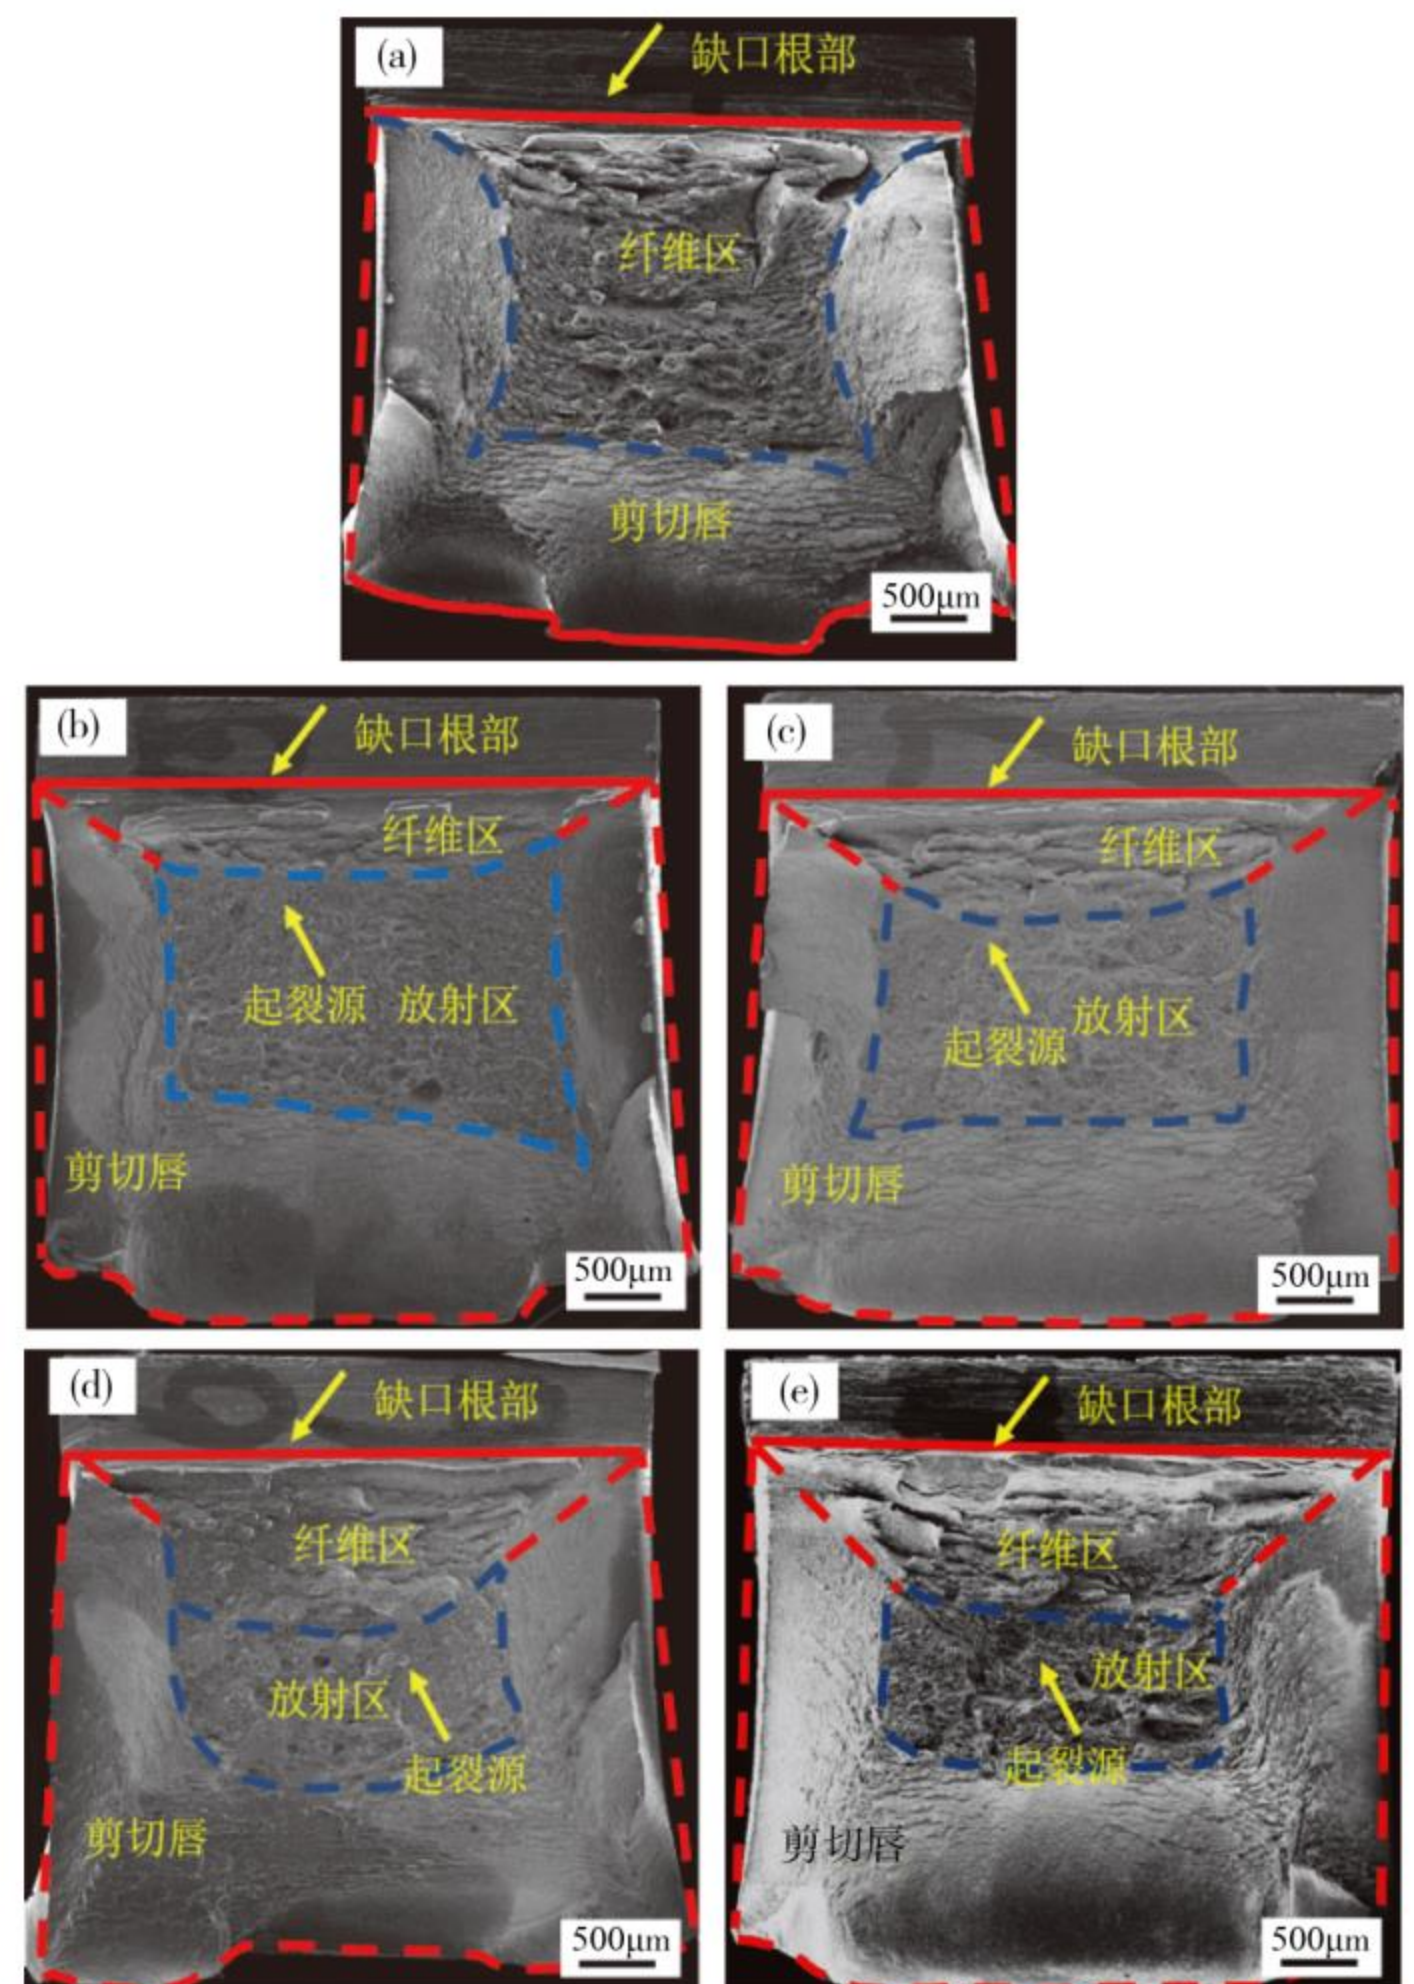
焊态和热处理态焊缝金属的冲击断口宏观形貌: (a) 焊态; (b) 580 °C; (c) 600 °C; (d) 610 °C; (e) 620 °C
